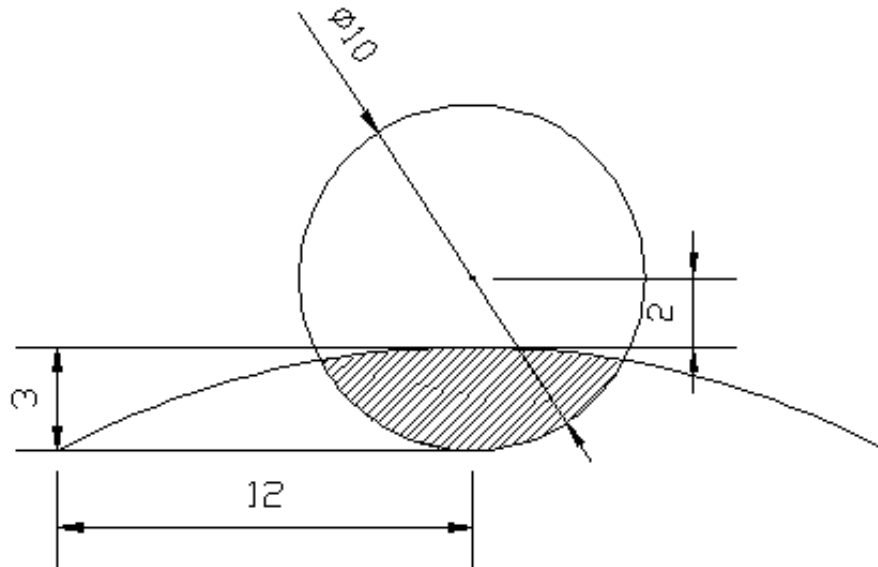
Vista transversal de la sección fisurada para la barra 15
